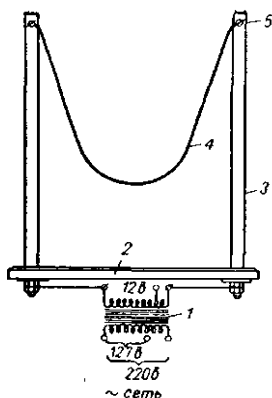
Электрическое приспособление для резки трубок: 1 — понижающий трансформатор; 2—изоляционная планка; 3—металлические стойки; 4—нихромовая проволока (нагреватель); 5—зажимы.
